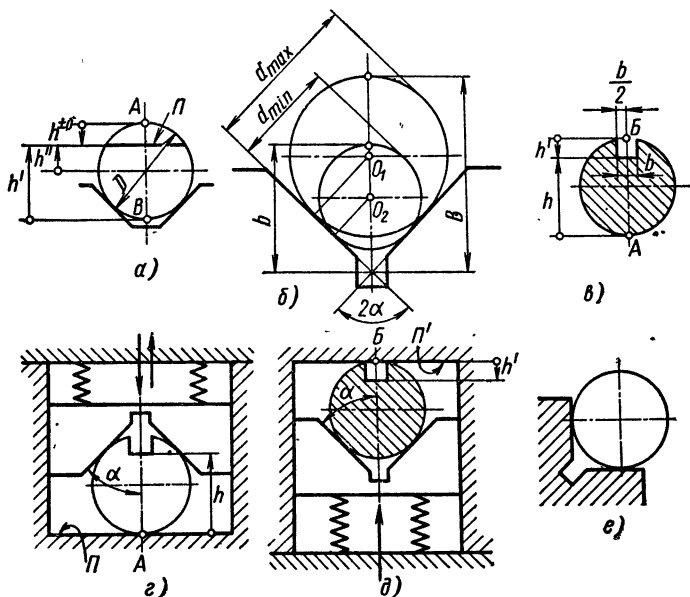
Схемы для определения погрешности установки деталей по наружной цилиндрической поверхности
